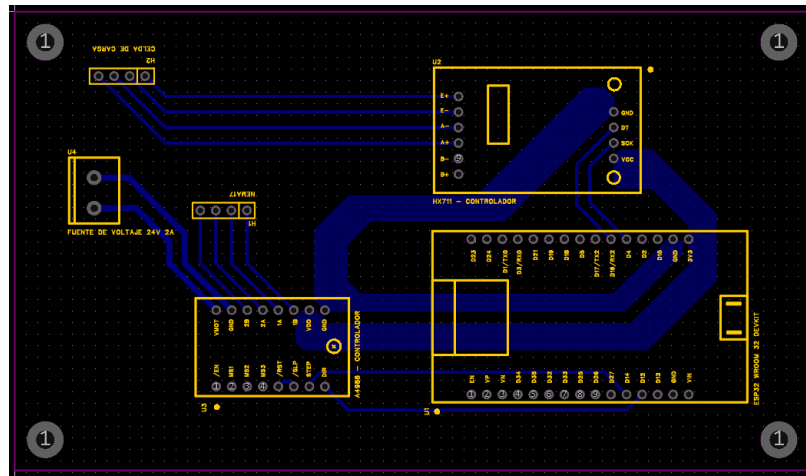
Disposición de componentes en la PCB para la máquina de ensayos
